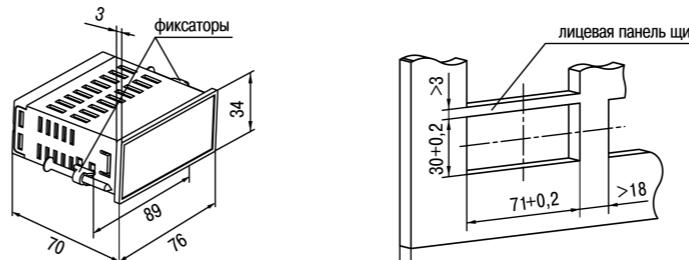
Габаритные размеры корпуса ЩЗ
